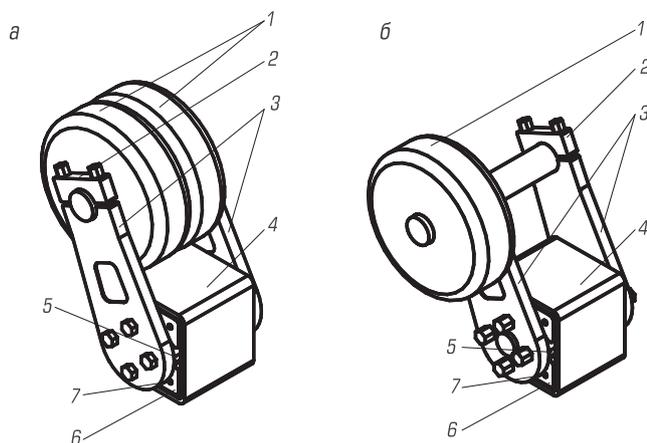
Роликовая направляющая нового типа для лобового (а) и бокового (б) направлений
